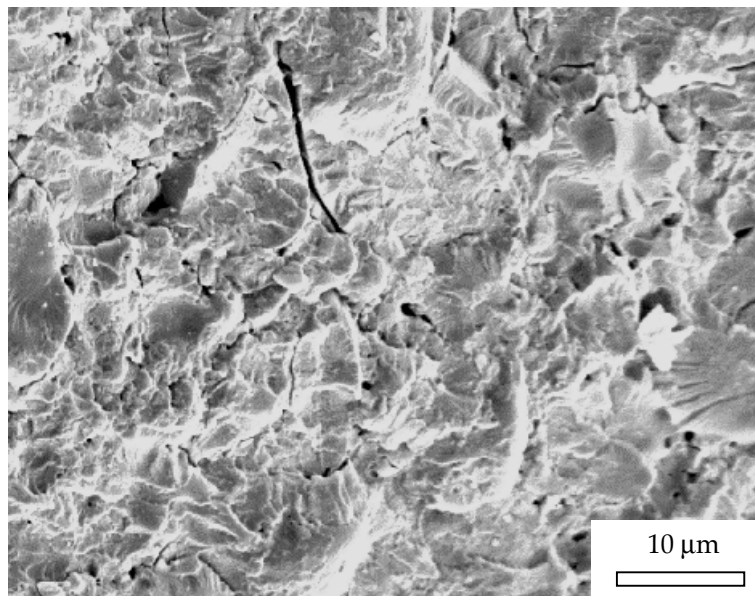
Detalle de la superficie de fractura. Zona alejada del defecto inicial.
